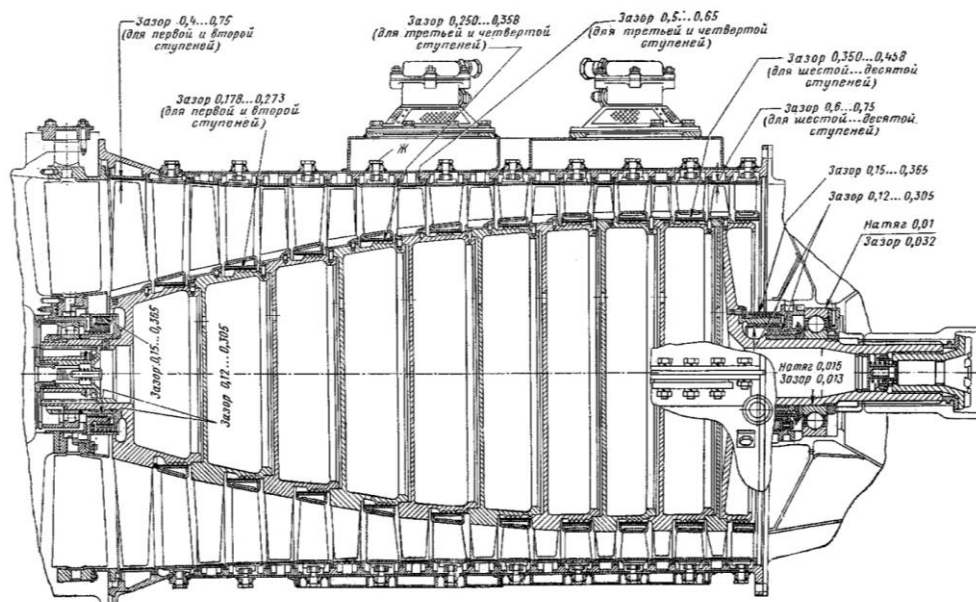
Продольный разрез компрессора ТВД со штифтовым креплением секций ротора, выполненных из стали, и со стальным сварным корпусом.
